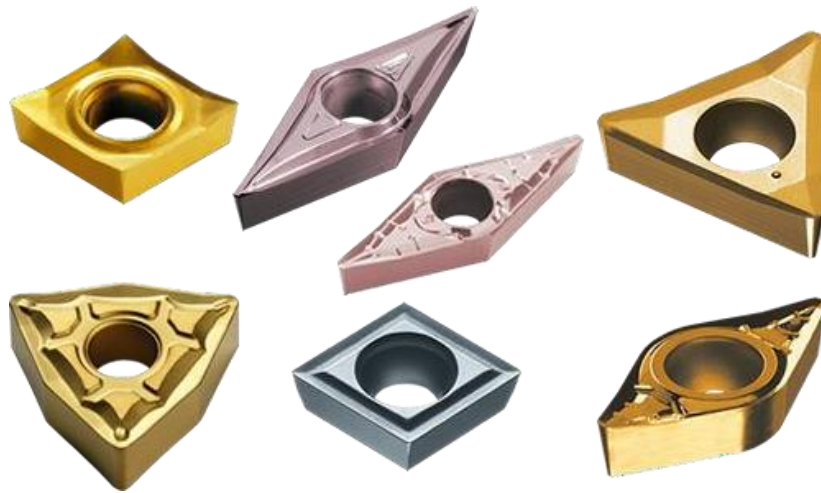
PLAQUETTES OUTILS EN CARBURES
